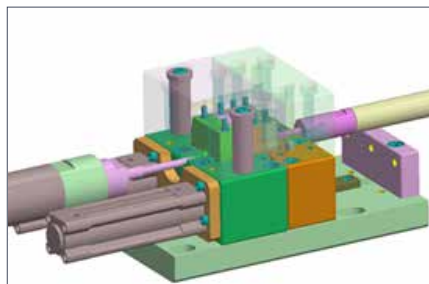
IHU-Werkzeug mit gedrehter Teilungsebene im CAD
